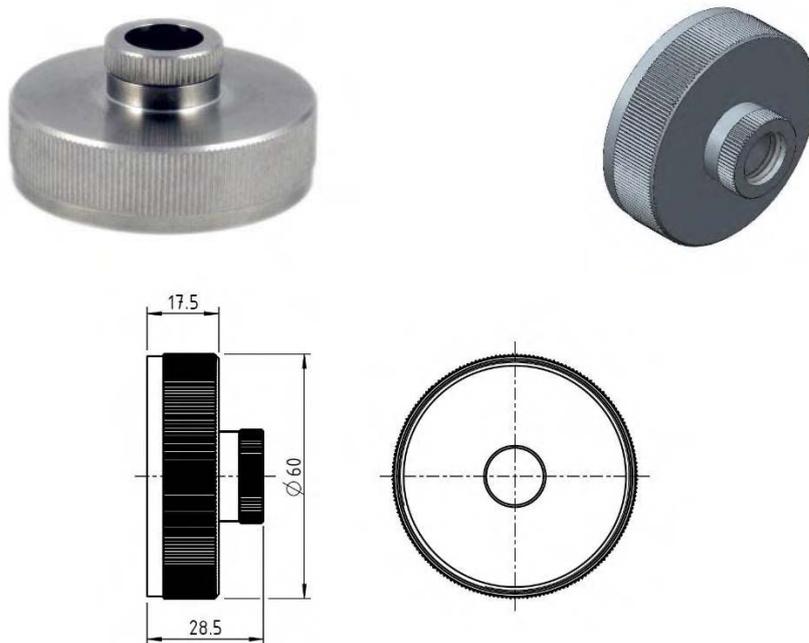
Vue et dimensions du verre polarisant pour couvercle arrière (E-PFEC)
